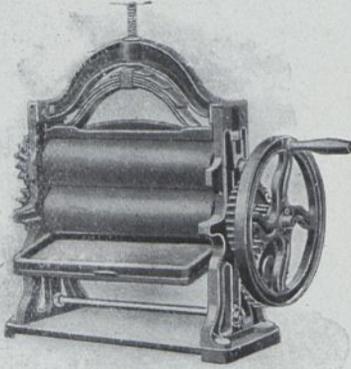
Einfaches Walzwerk von D. Bridge & Co.
